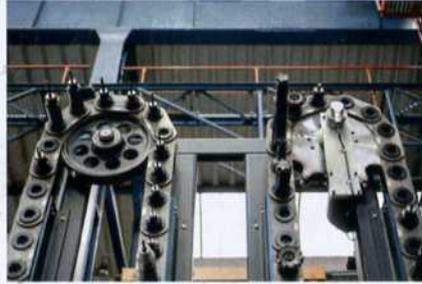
Werkzeugwechselsystem für bis zu 120 Werkzeuge
